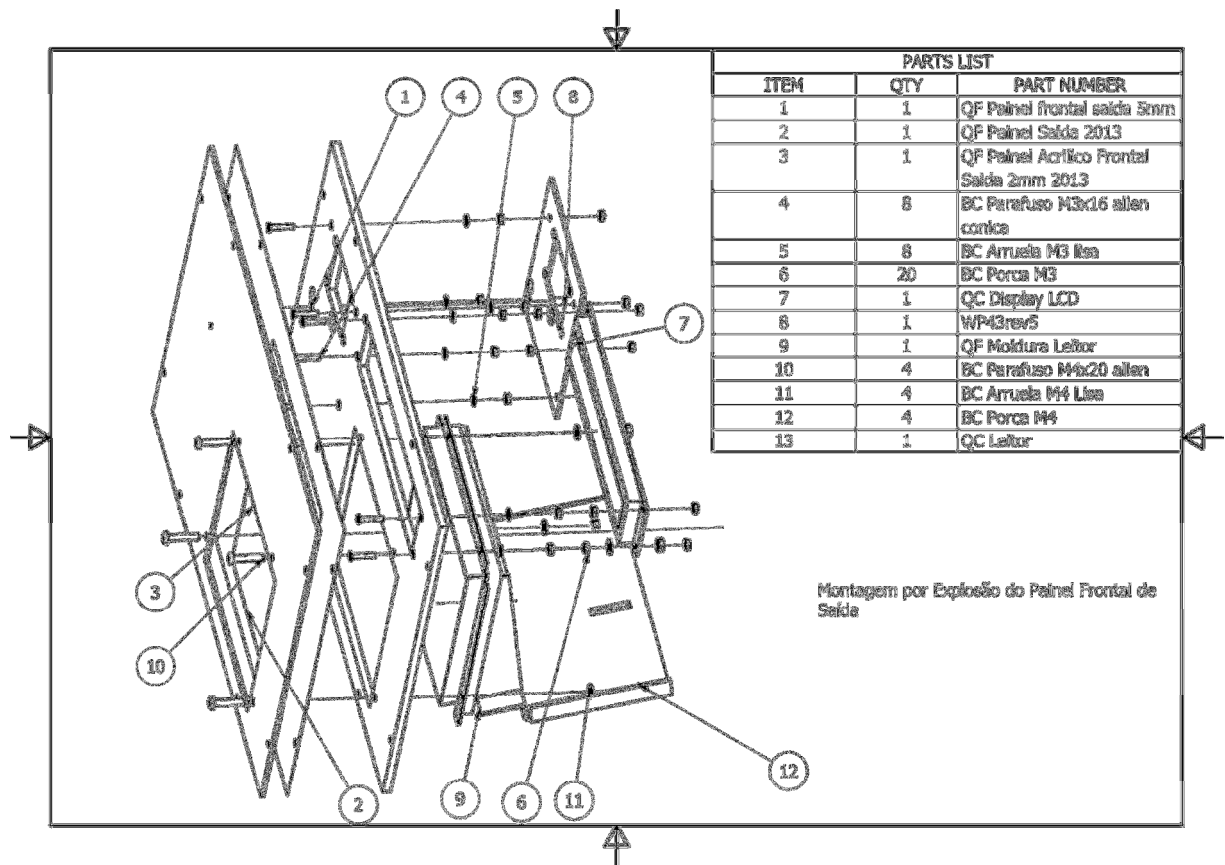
Montagem do Painel Frontal de Saída em Explosão
